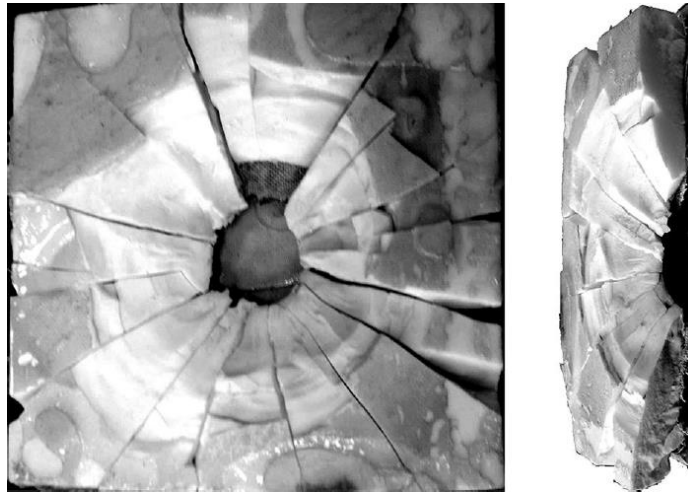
Fractura de una sección de alúmina tras el impacto de una bala perforante de un diámetro de 7.62 mm [19]
